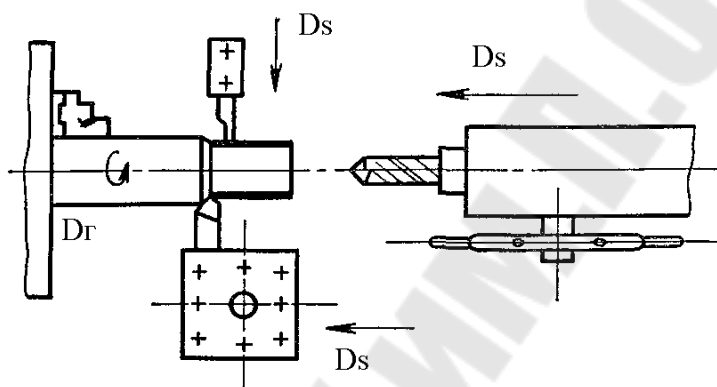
Схема обработки на токарно-сверлильно-отрезном станке
